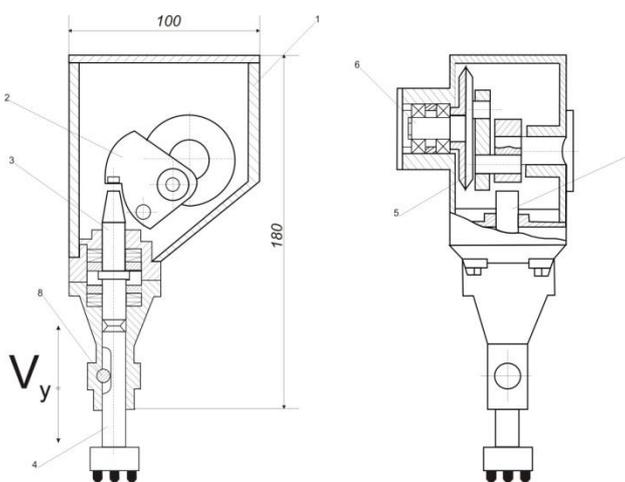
Общий вид ударного узла.: 1-корпус; 2-ударник; 3-хвостовик; 4-инструмент; 5-колесо; 6-муфта; 7-буksа; 8-фиксатор.
